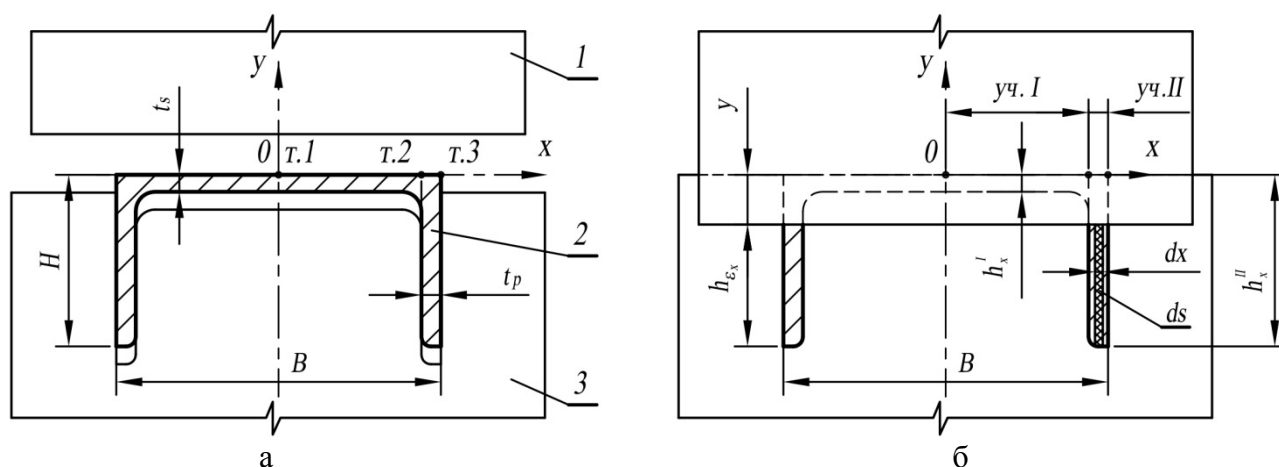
Схема к определению силы резки швеллера фасонными ножами; а – расположение ножей и заготовки до начала резки; б – в процессе резки
